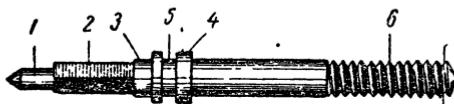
Схема изготовления заводного валика: 1—конец валика; 2—квадратная грань заводного валика; 3—заплечик заводного триба; 4—заплечик, находящееся в платине; 5—выточка для крепления винта или переводного рычага; 6—резьба для головки
